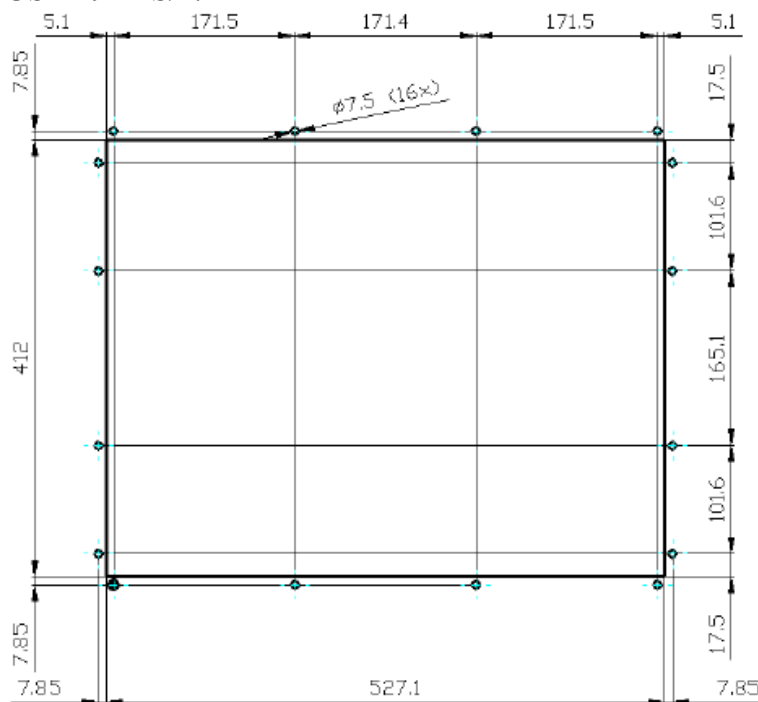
Схема расположения отверстий монитормного кожуха рабочей станции.
